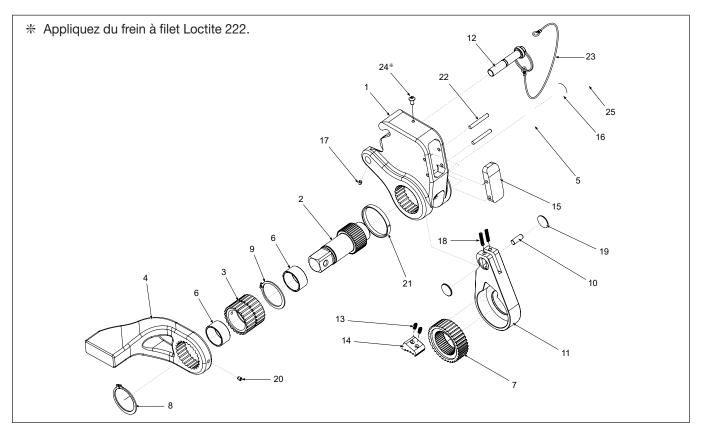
vue éclatée de la cassette HSQ de la clé HMT
